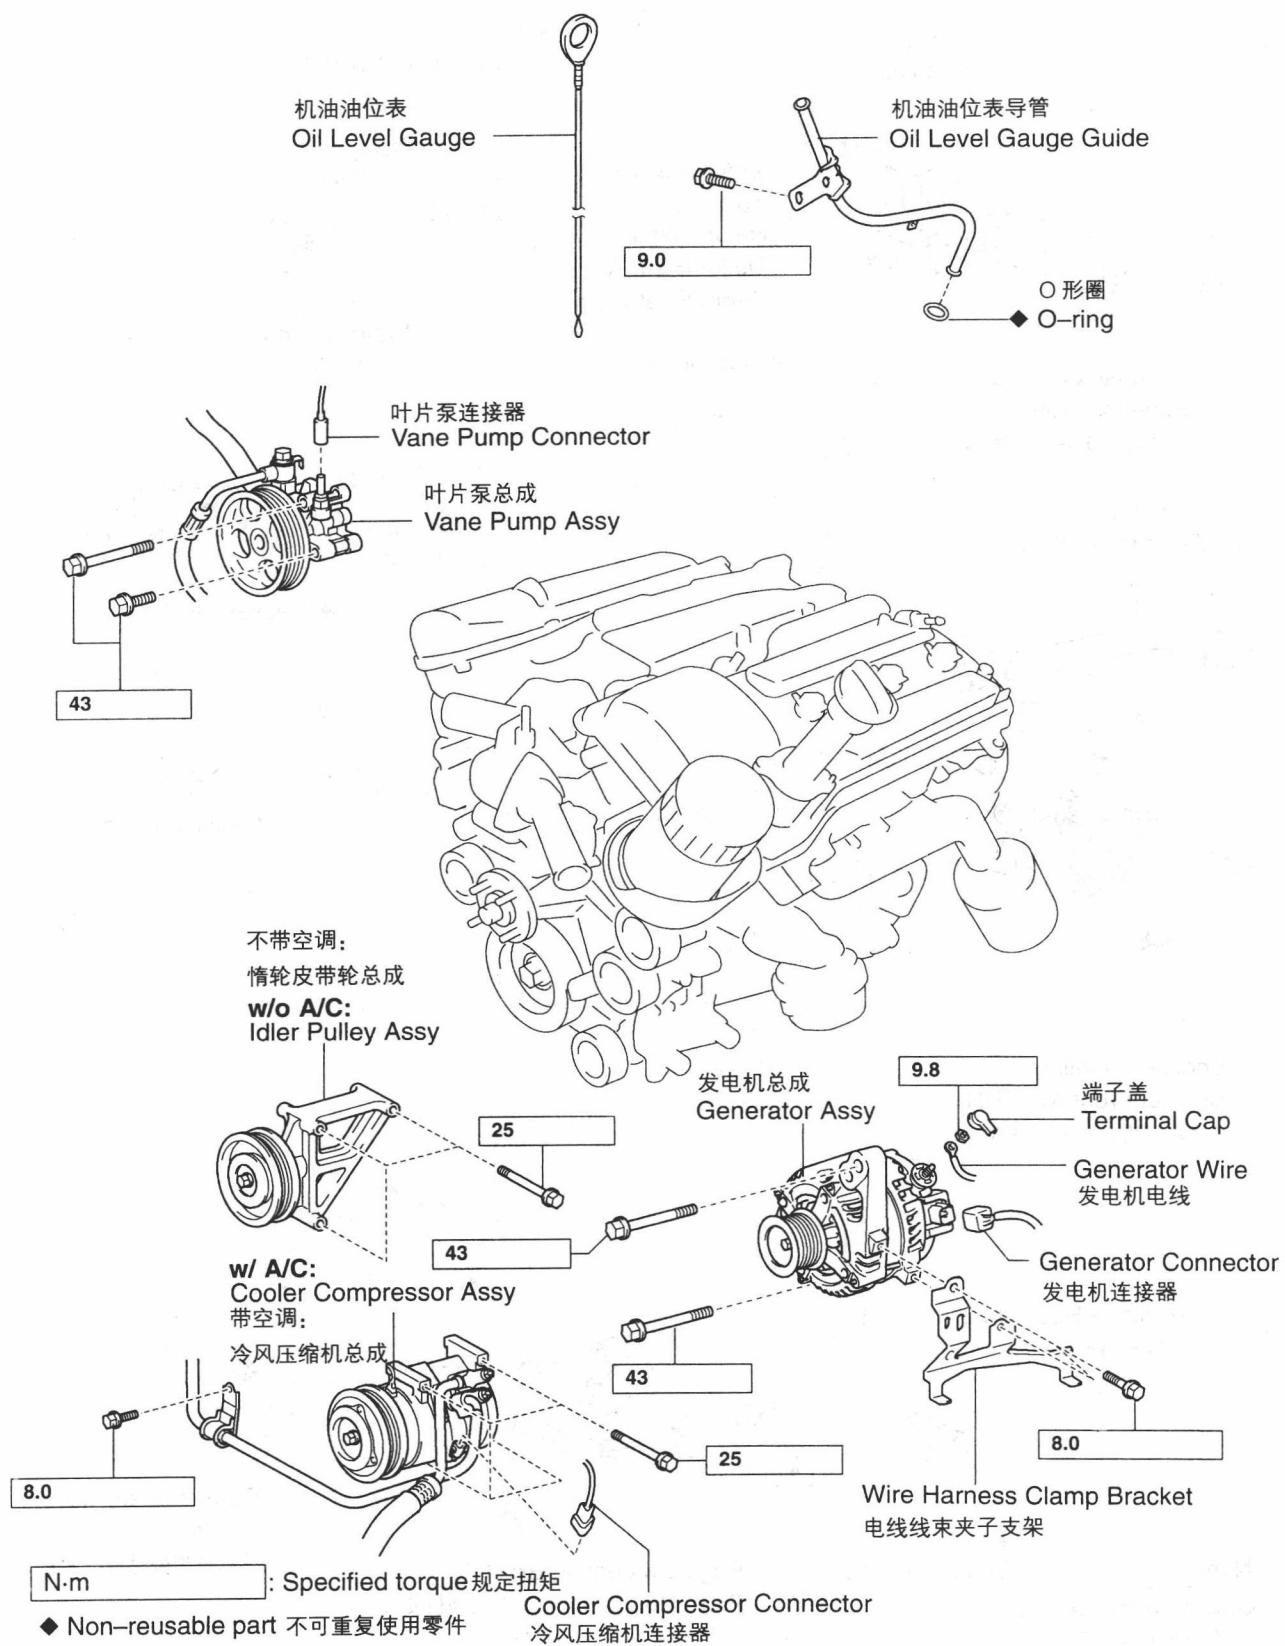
发动机总成 (ENGINE ASSEMBLY) (3)
